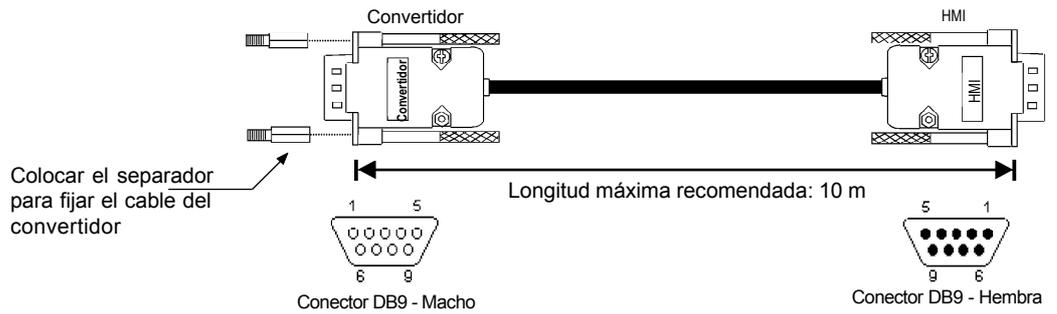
Cable para uso remoto del HMI ≤ 10 m
